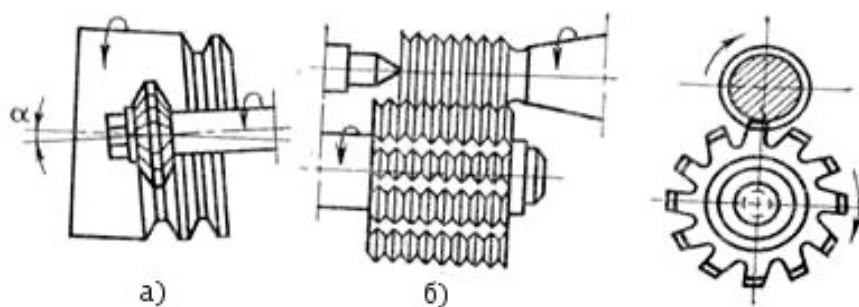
Фрезерование резьбы: а) – дисковой фрезой; б) – групповой фрезой.
